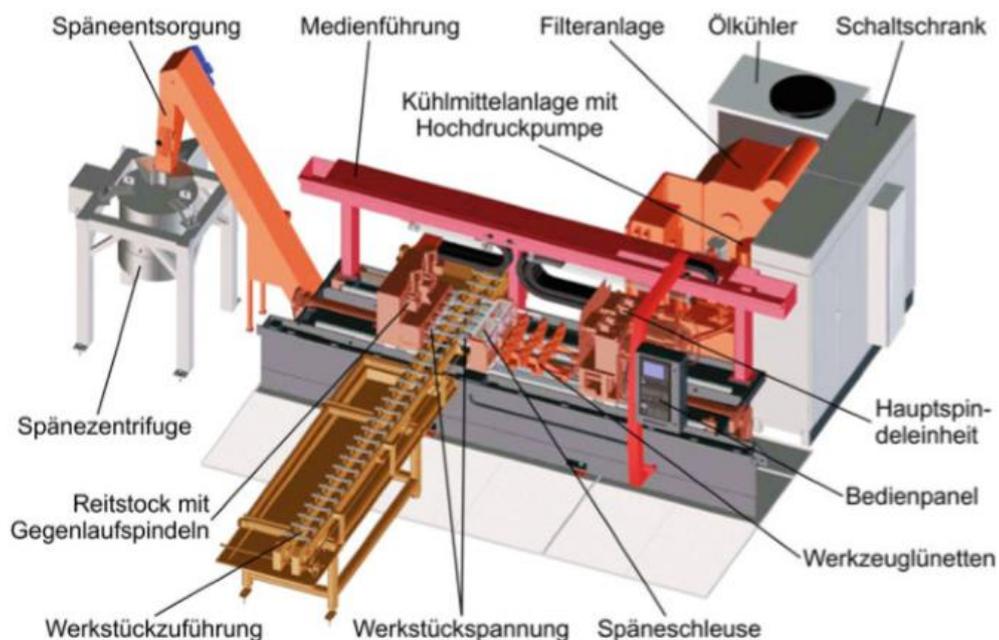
Mehrspindlige Produktionstiefbohrmaschine^[9]
